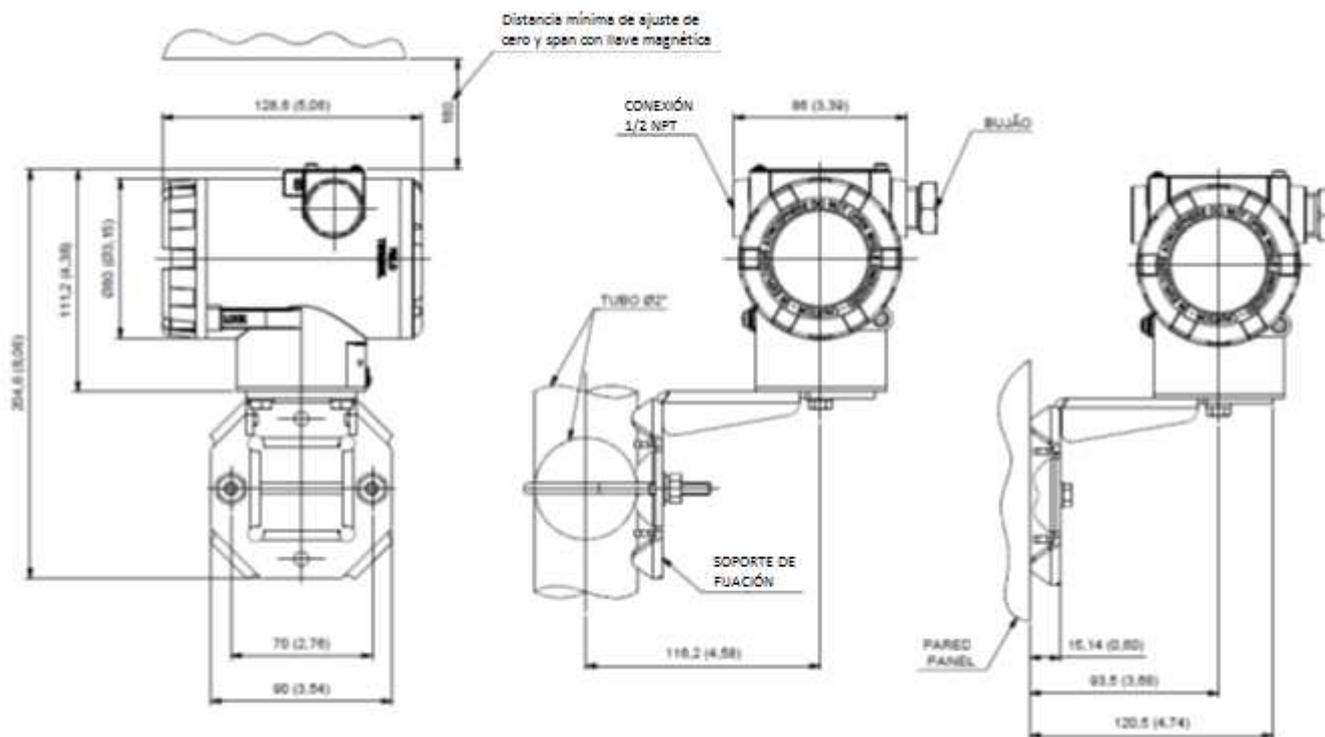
Diseño dimensional y esquema de montaje del VTT10-FP.
